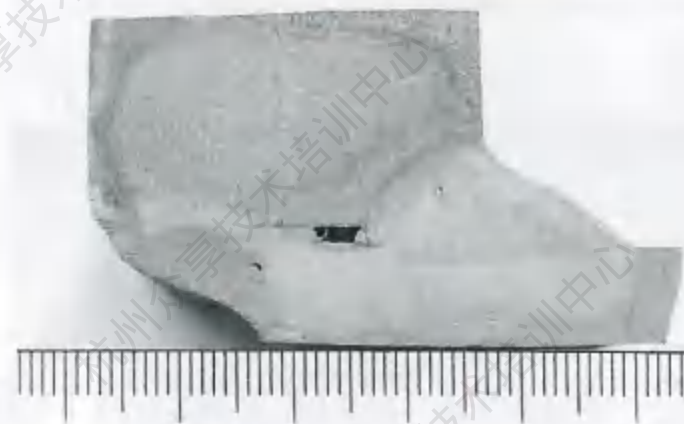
焊缝根部未焊透、气孔、坡口未熔合
